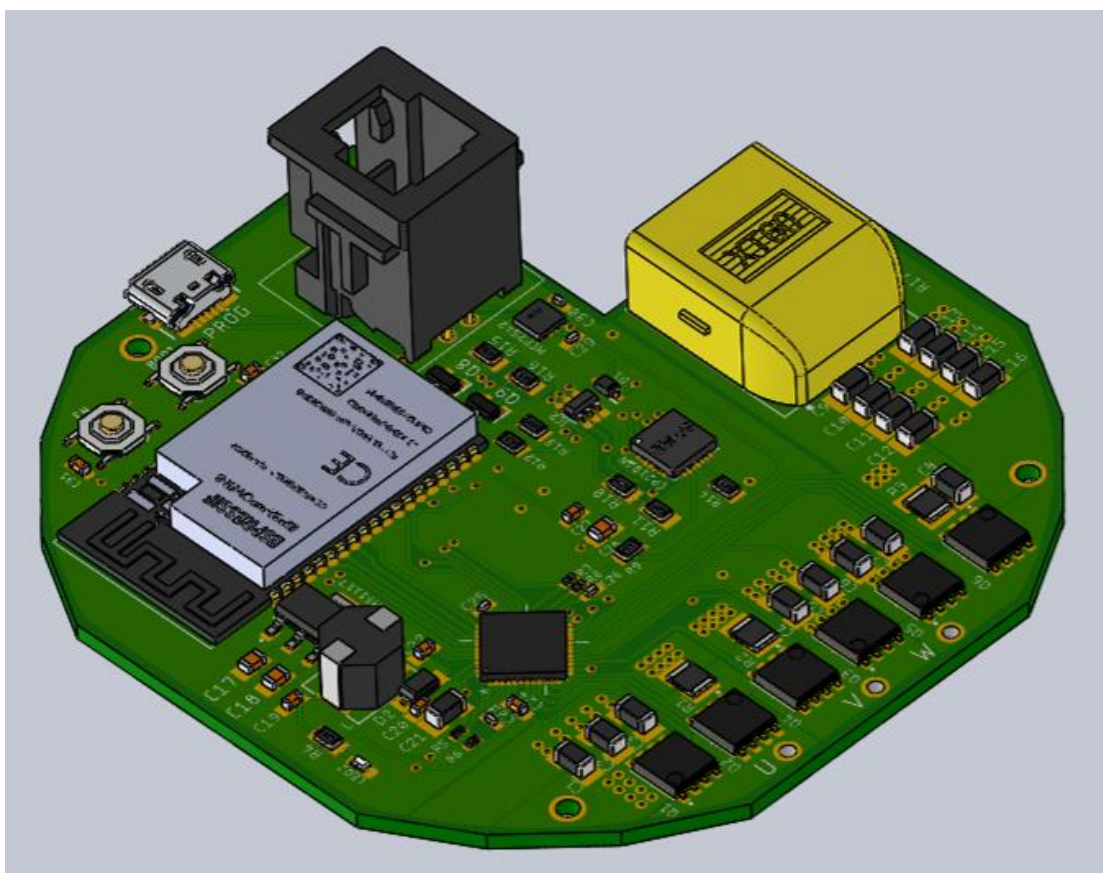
Vista 3D de la PCB (Font: Ernest Porqueras)
